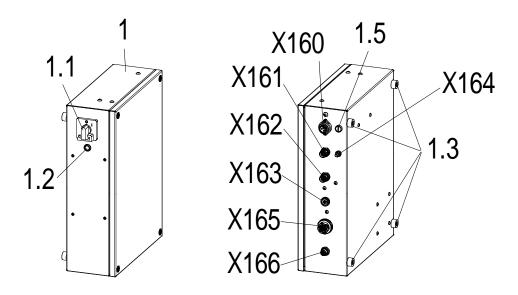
Vue avant et arrière de l'unité de contrôle
